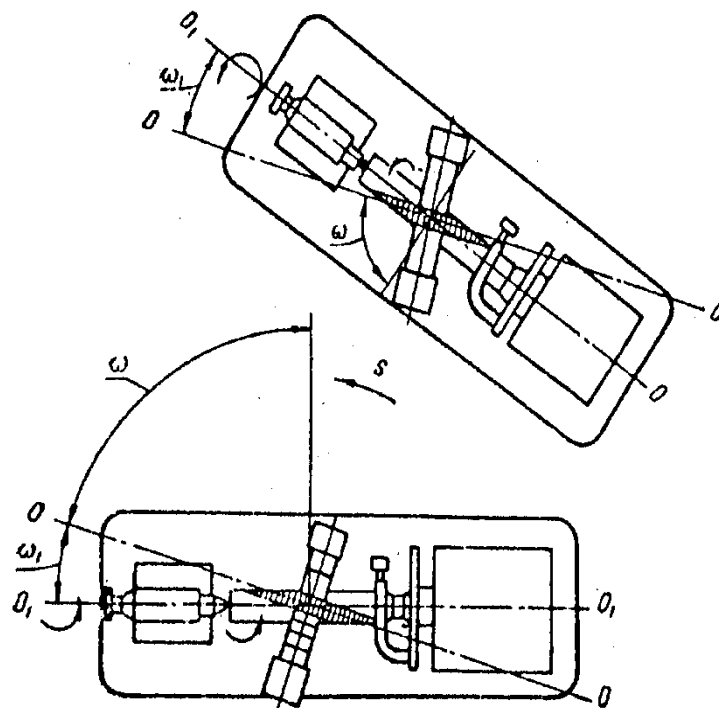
Схема повороту стола при фрезеруванні гвинтових канавок
